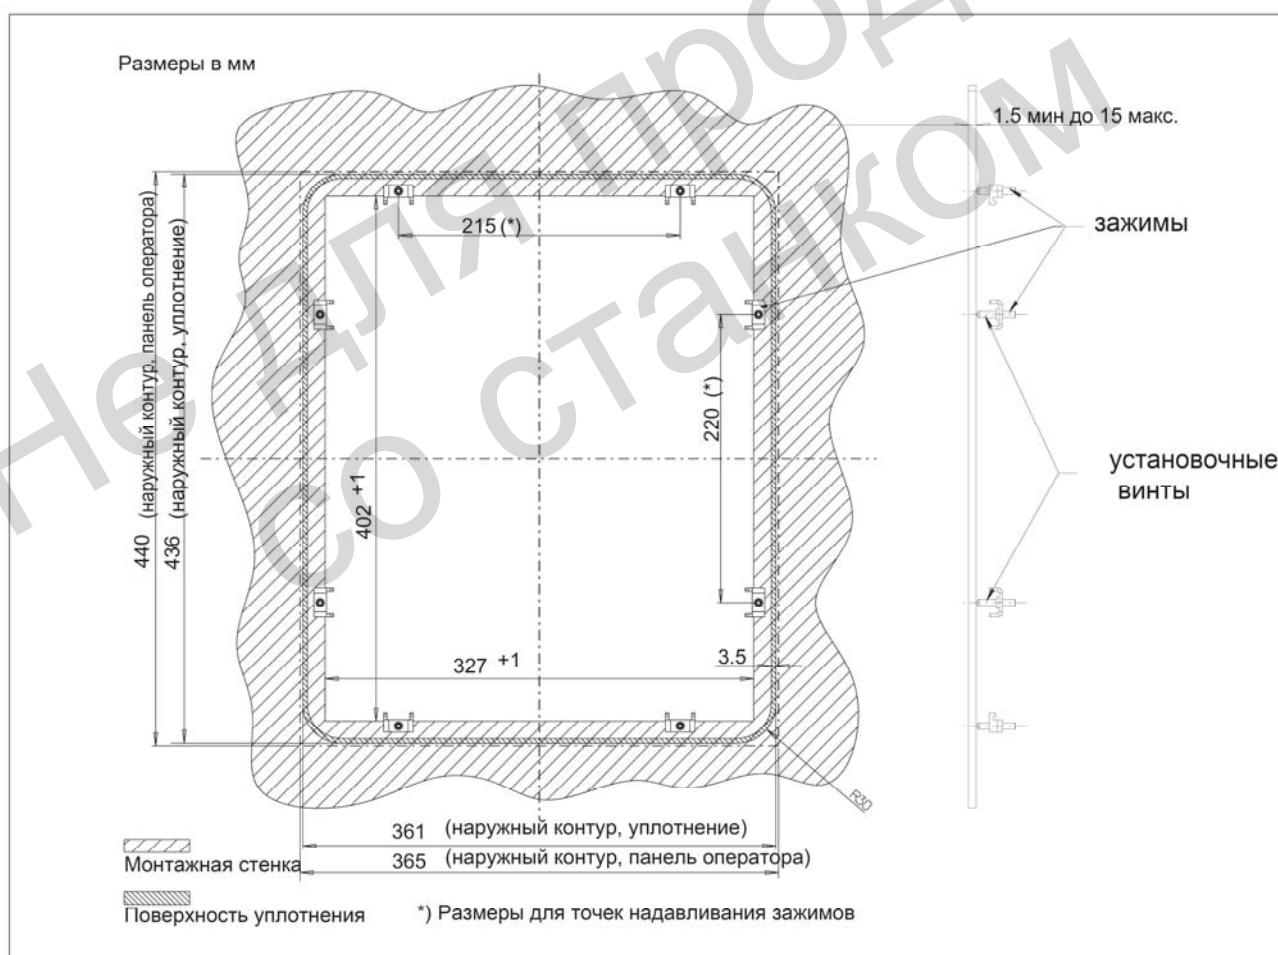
Габаритный чертеж для монтажа панели оператора OP 012T
